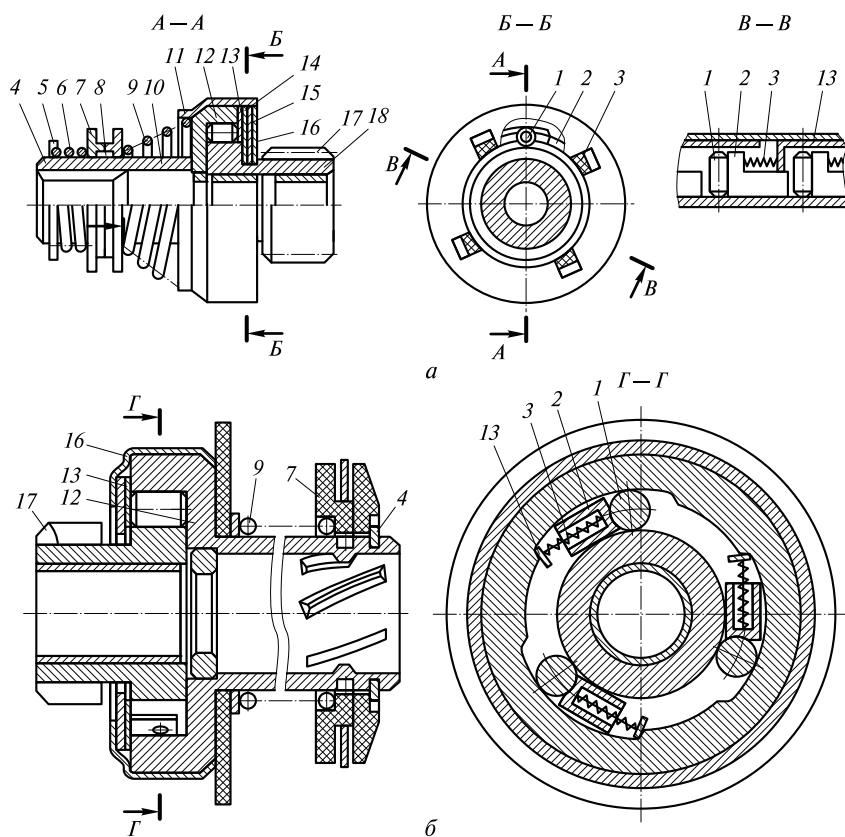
Конструкции роликовых муфт свободного хода приводных механизмов стартеров:
